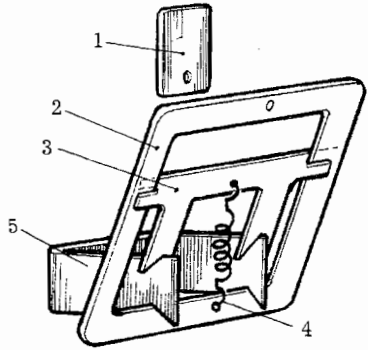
Конструкция кулачкового механизма выключателя с плоской пружиной: 1 — ручка; 2 — пружина; 3 — контактная пластина.
